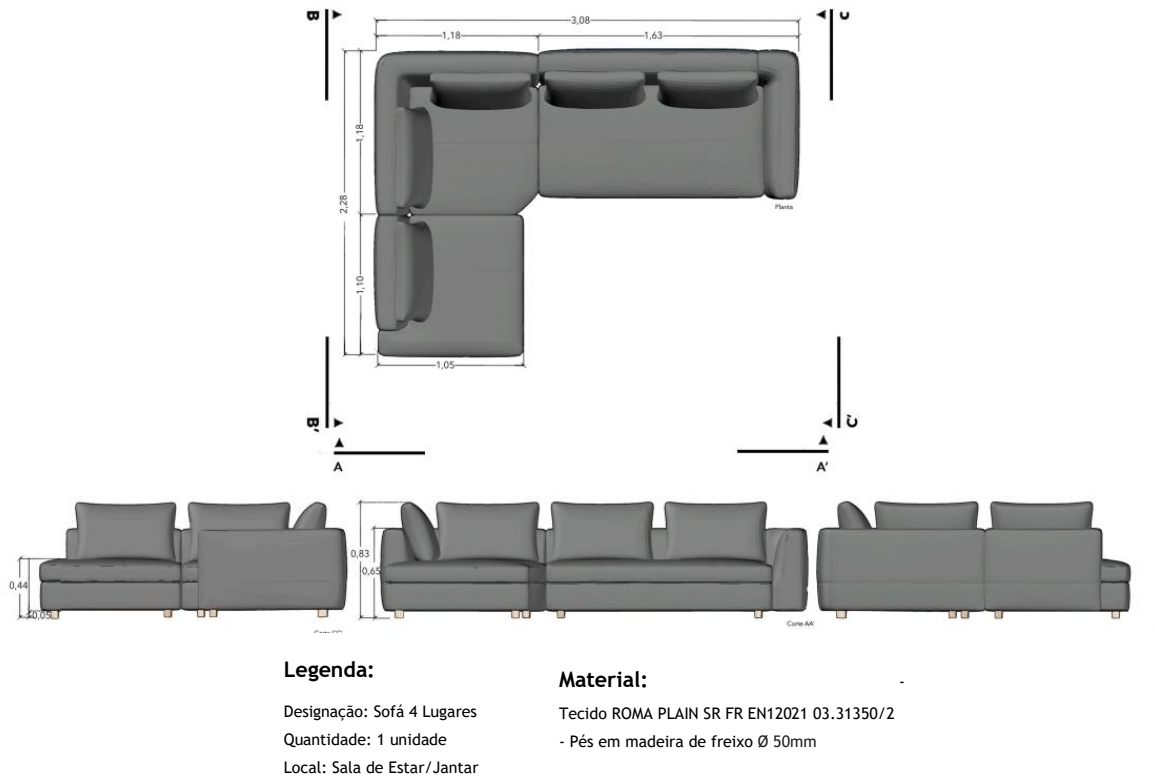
Desenho Técnico Sofá. Fonte: Homestories
